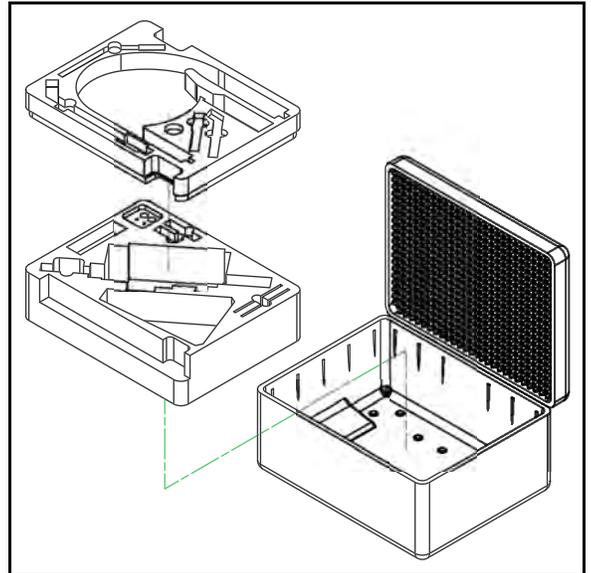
DETALLE DEL MALETÍN DE TRANSPORTE DE LA BW2600
